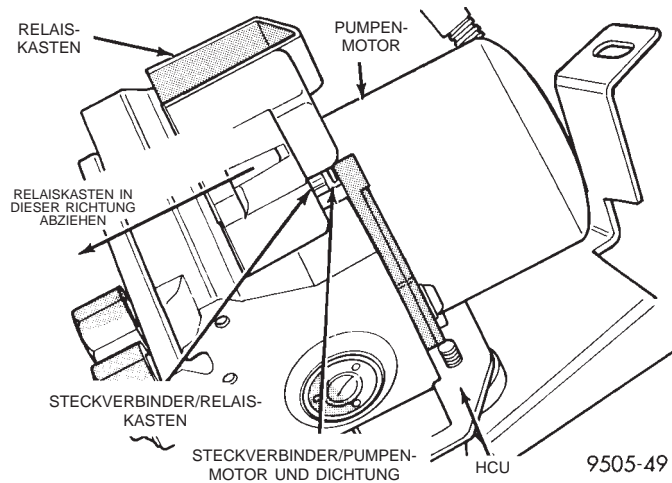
Schrauben zur Befestigung des Relaiskastens an der HCU
